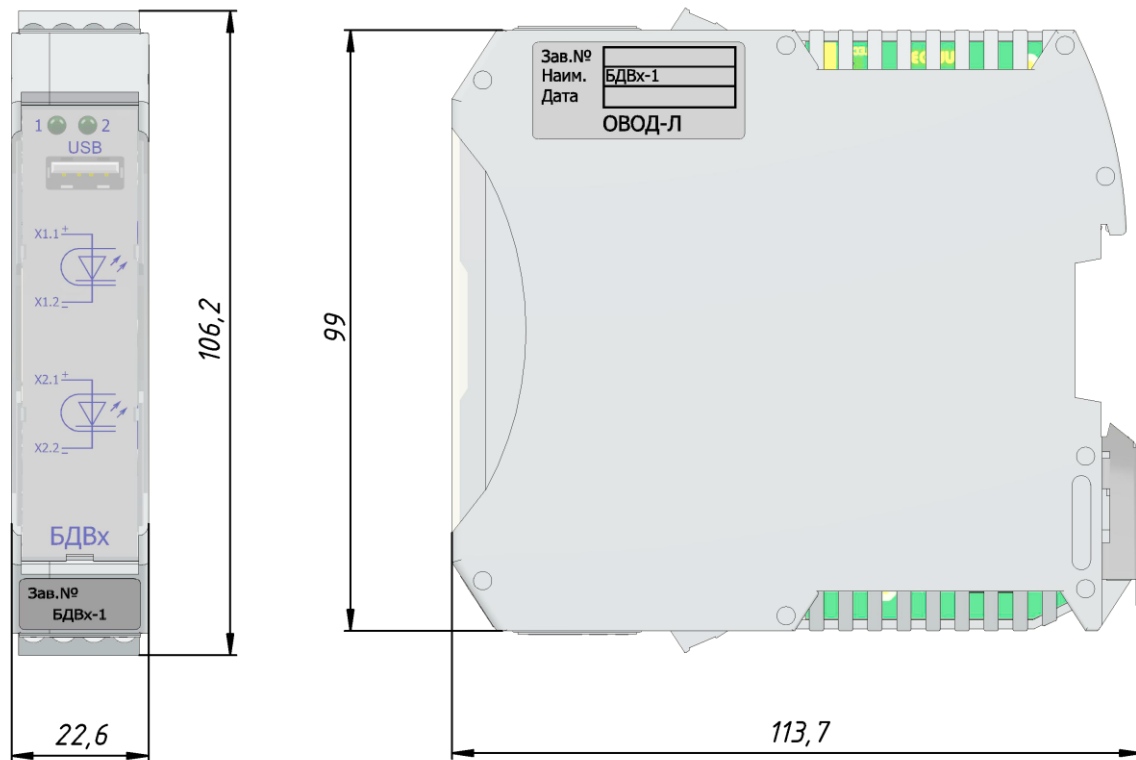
Внешний вид и габаритные размеры БДВх
